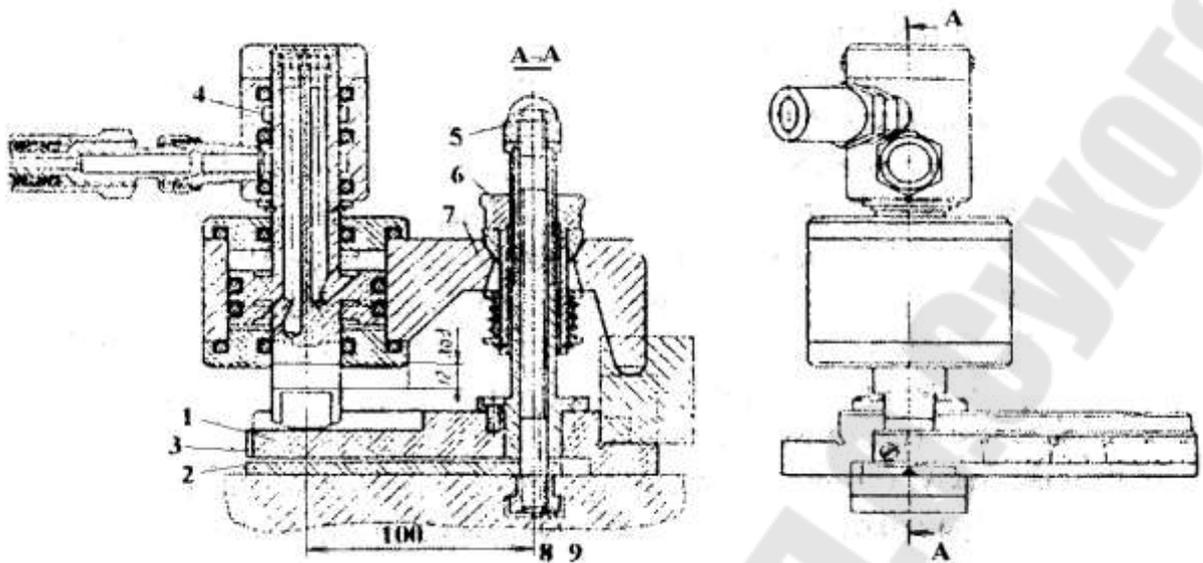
Гидравлическое приспособление для закрепления резцов на столе полуавтомата мод. 311624.
